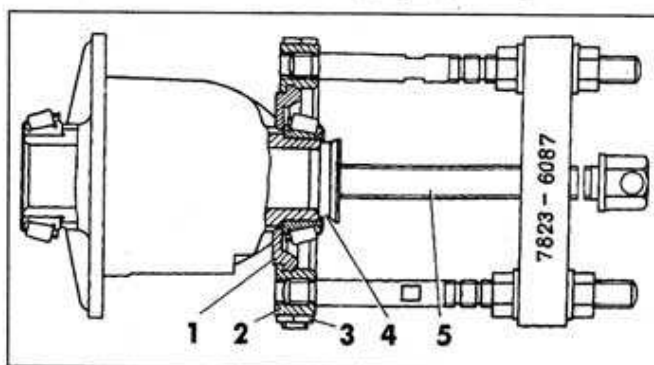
Снятие внутреннего кольца подшипника с коробки дифференциала:
